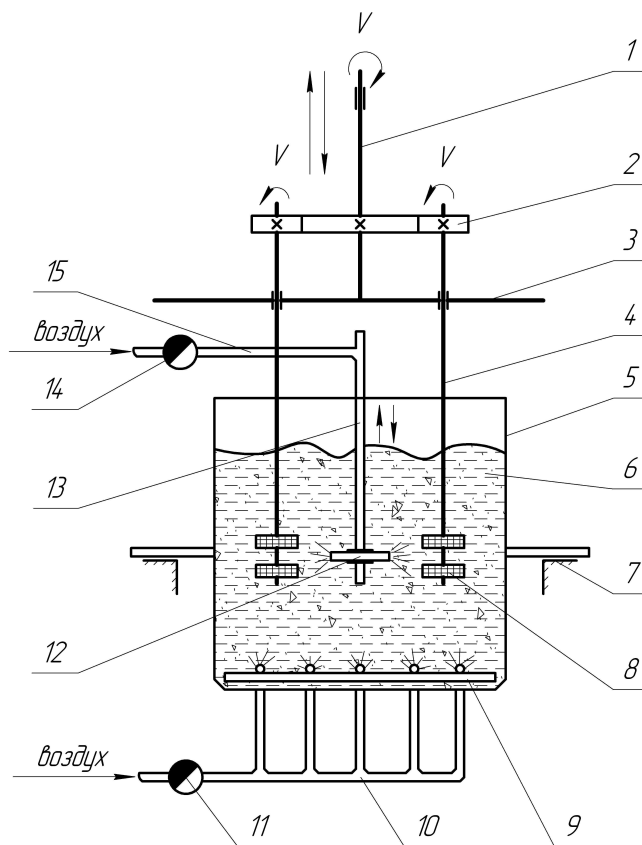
Принципиальная схема устройства для реализации нового способа гидроабразивной обработки затопленными струями. 1 – шпиндельное устройство; 2 – зубчатая передача; 3 – многоместное приспособление; 4 – установочные пальцы; 5 – резервуар; 6 – рабочая среда; 7 – жесткая опора; 8 – обрабатываемые детали; 9 – барботажная система; 10, 15 – гибкие трубопроводы; 11, 14 – дроссели; 12 – эжекционное сопло струйного аппарата; 13 – штанга
